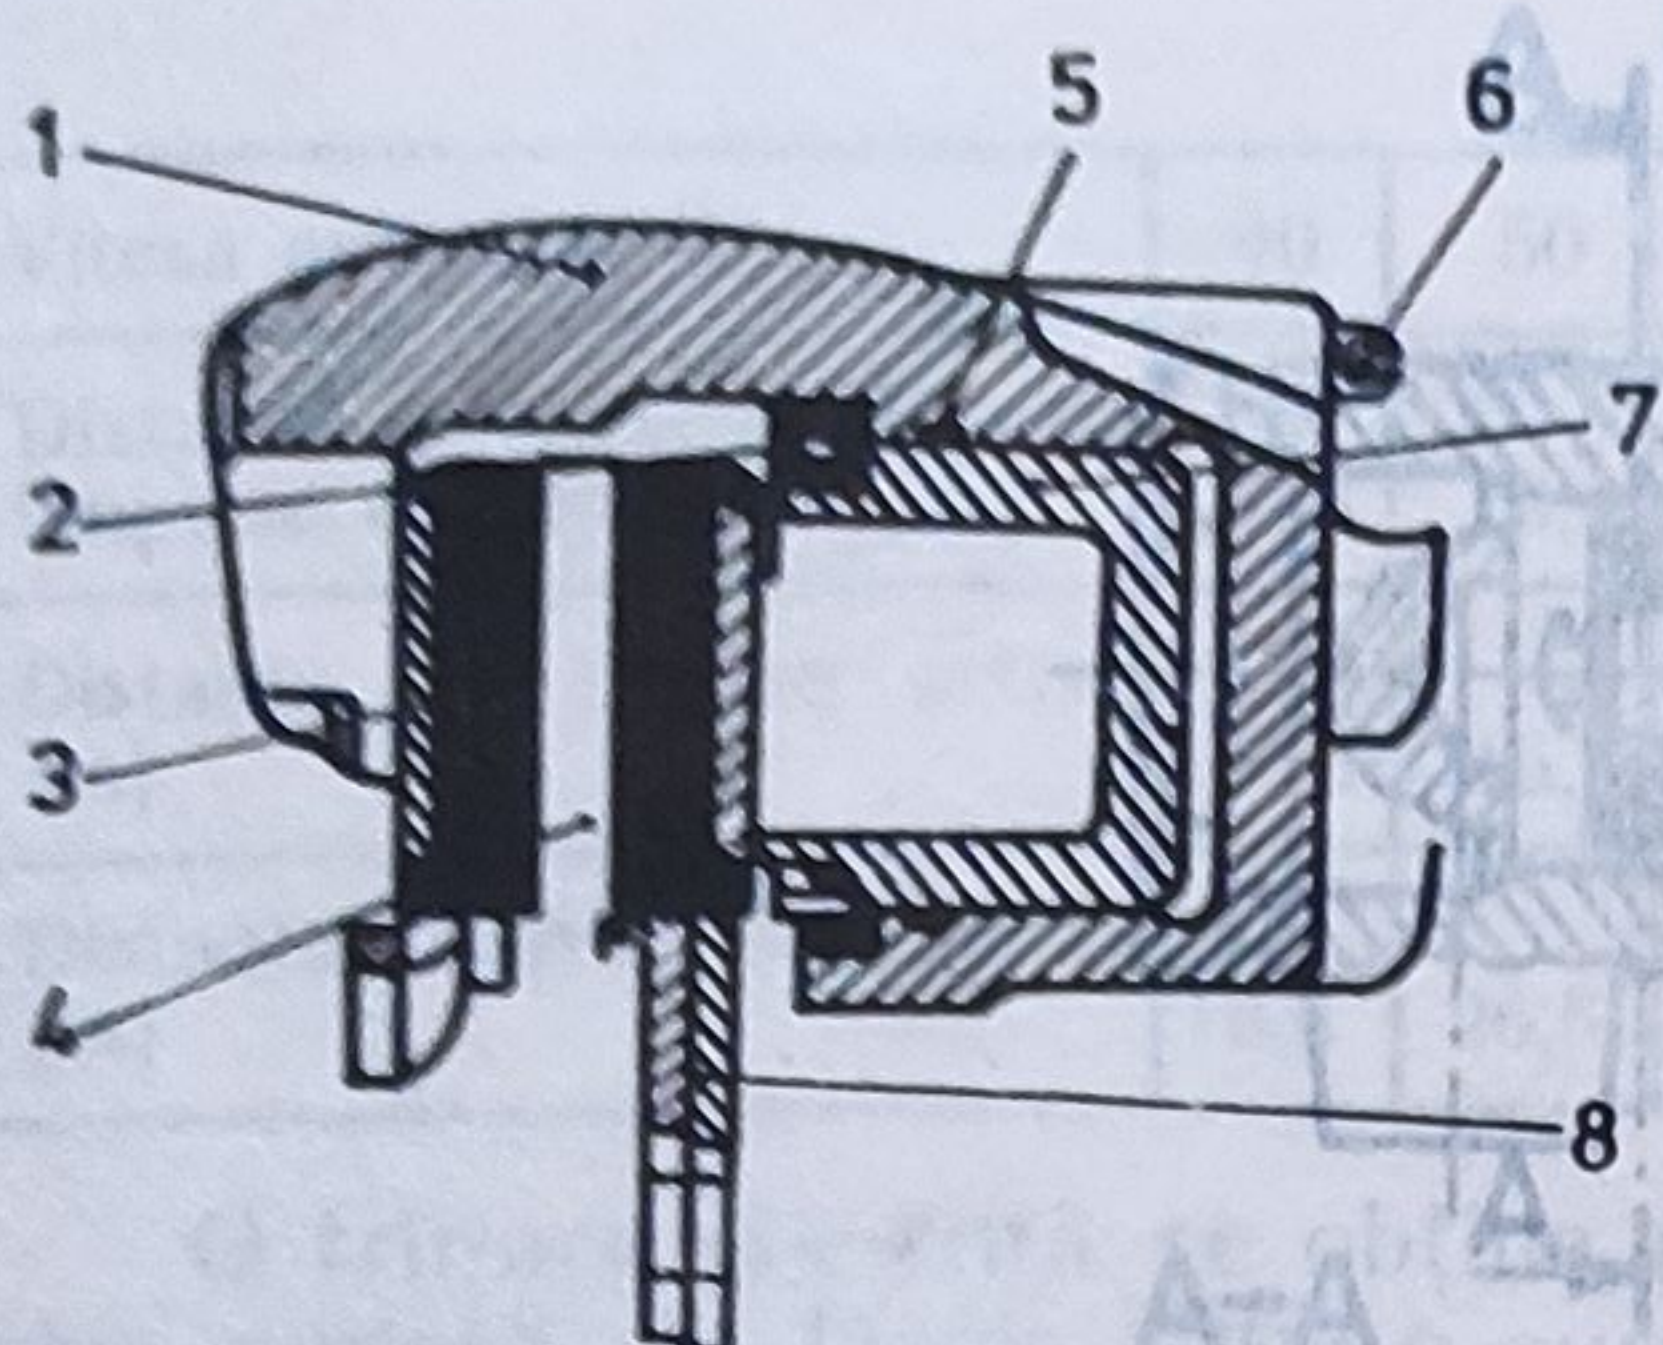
Etrierul de frână față (asamblat); 1—corpul etrierului; 2—burduf de etanșare; 3—ferodou; 4—disc de frână; 5—garnitură de cauciuc pentru etanșare; 6—orificiul racordului flexibil; 7—pistonul etrierului; 8—flanșă
